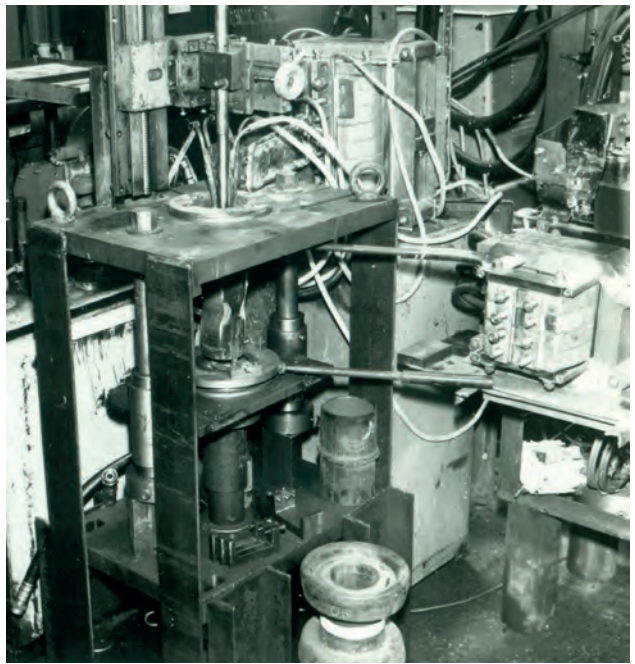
Лабораторна установка індукційного зварювання за допомогою внутрішнього індуктора
